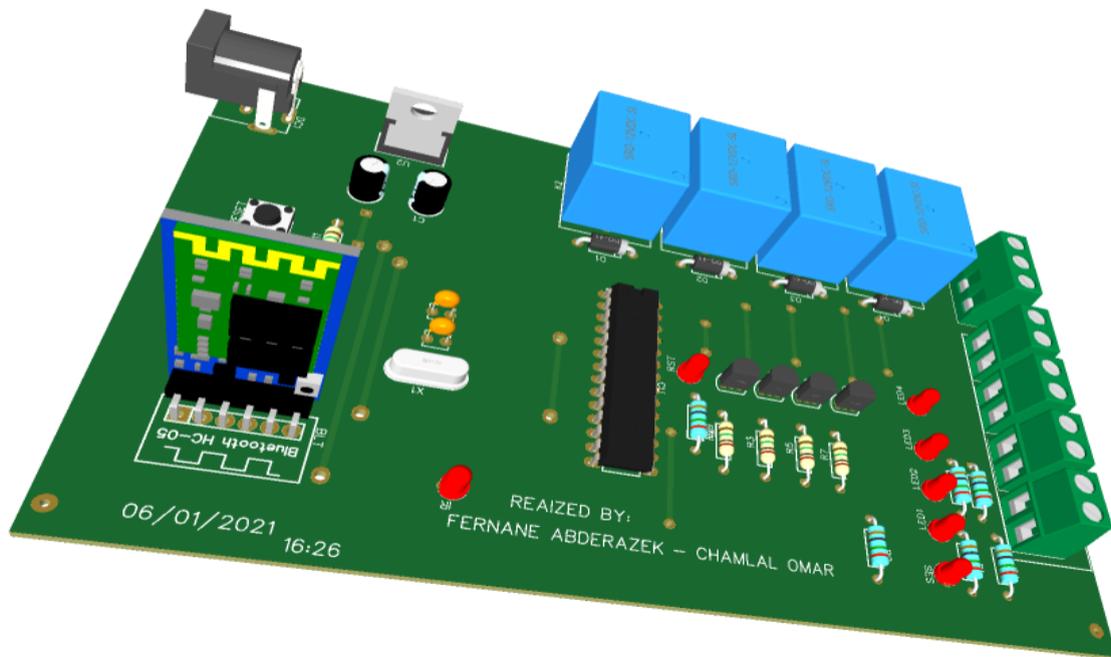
Carte PCB en 3 Dimensions 'Côté Droit'
